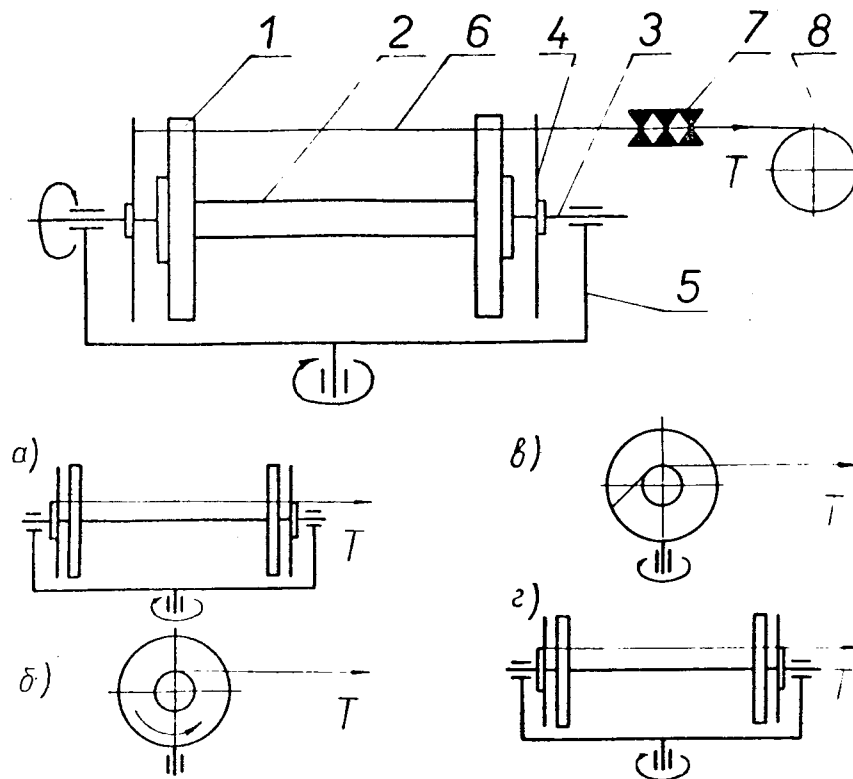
Схема устройства для намотки камер. 1 - фланец камеры; 2 - распорный элемент; 3 - полуось; 4 - шаблон; 5 - поворотная вилка; 6 - проволочка; 7 - устройство для очистки проволоки; 8 - bobина с проволочкой и натяжное устройство. а, б, в, г - последовательность операций намотки проволочек.
